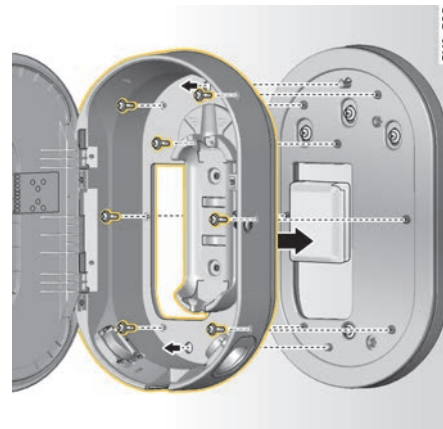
Vissage de la borne de recharge à la plaque de montage
